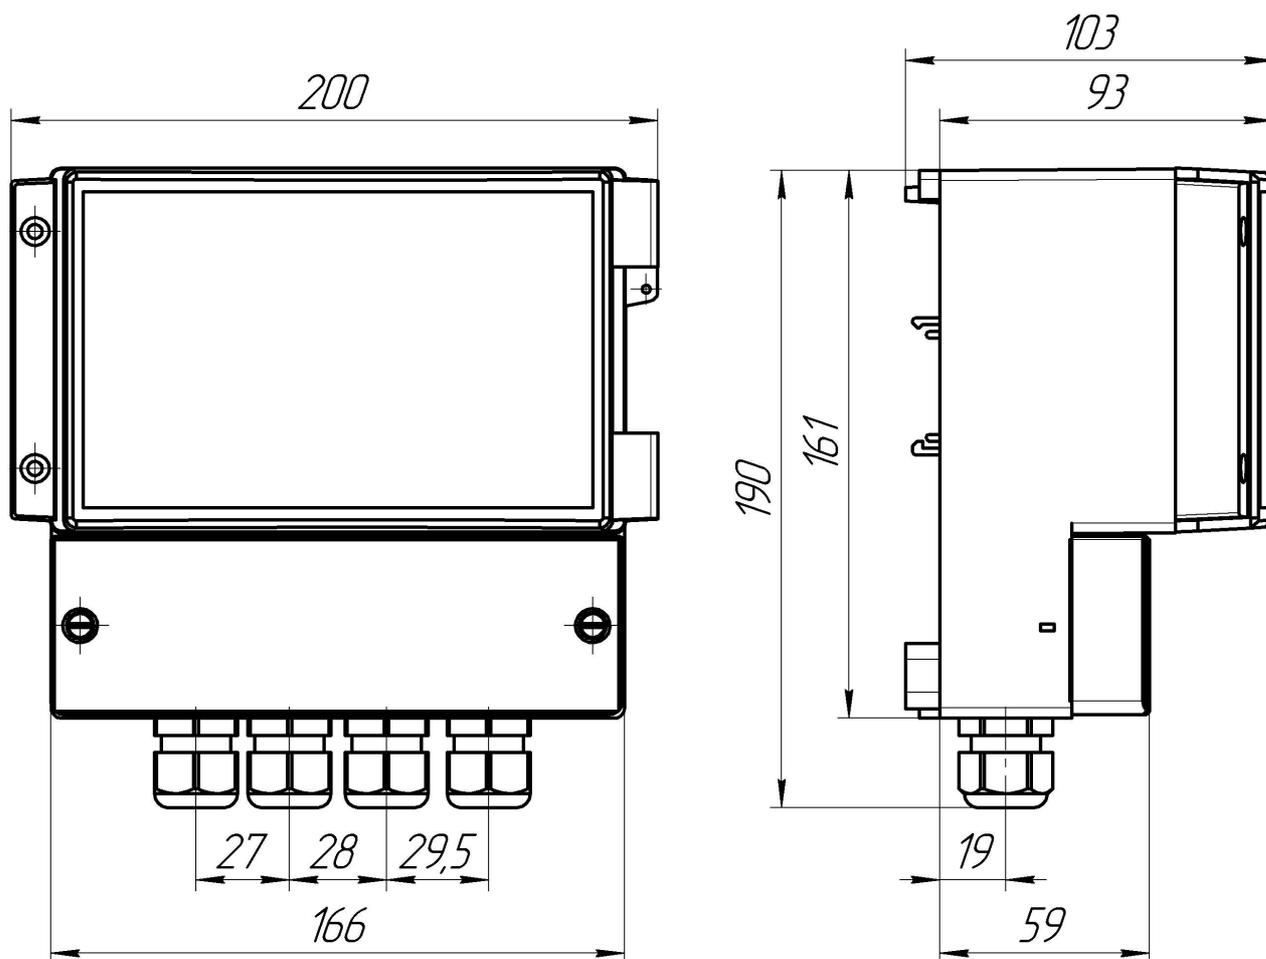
Габаритные и монтажные размеры корпуса ИП настенного исполнения
